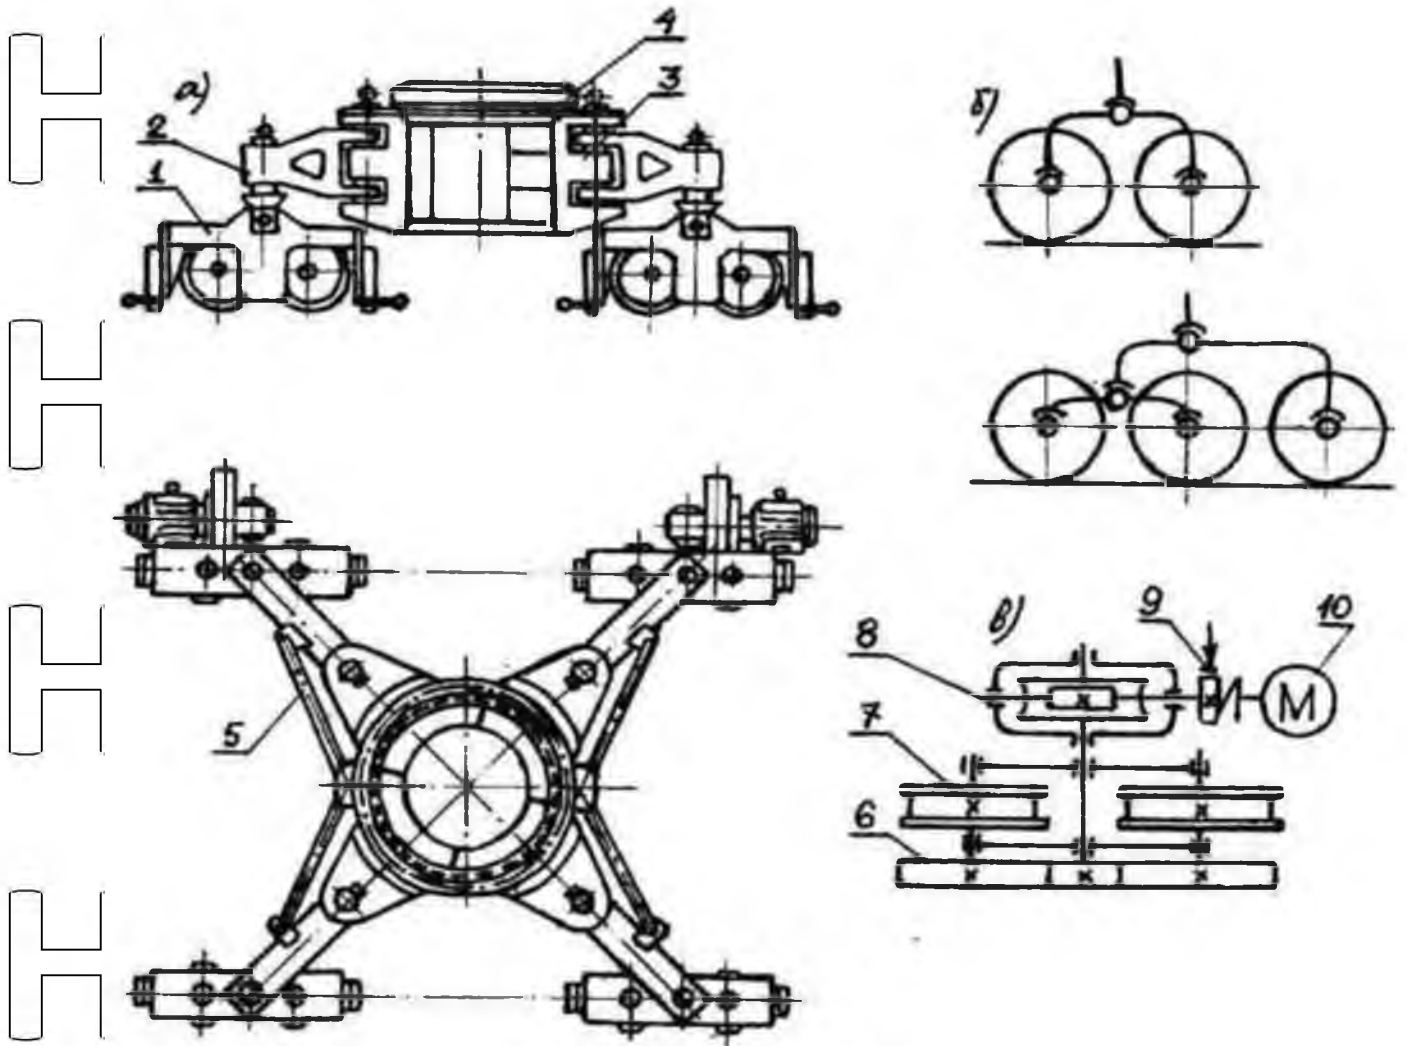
Опорна частина баштових кранів із поворотною платформою: а - загальний вигляд; б - схема балансирних ходових візків; в - кінематична схема механізму пересування. 1- ходовий візок; 2 - шарнірний кронштейн; 3- ходова рама; 4- опорно-поворотний пристрій; 5 - тяга; 6 - зубчаста передача; 7- ходове колесо; 8- черв'ячний редуктор; 9- муфта з гальмом; 10 - електродвигун
